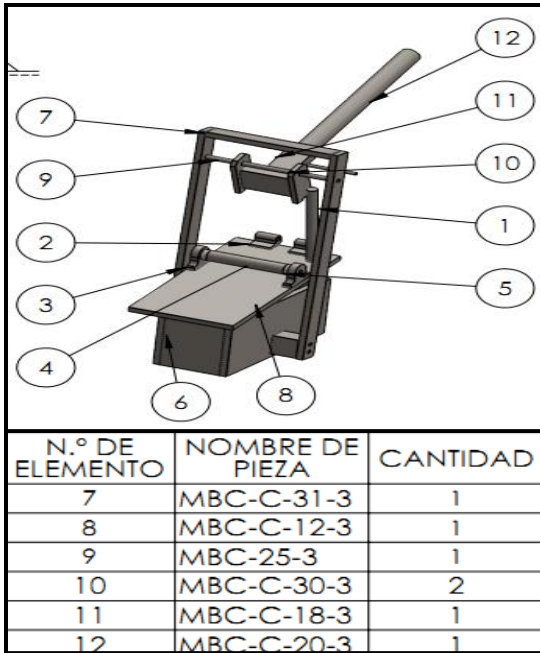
Indicación de soldadura del ensamble tapa con movimiento.
